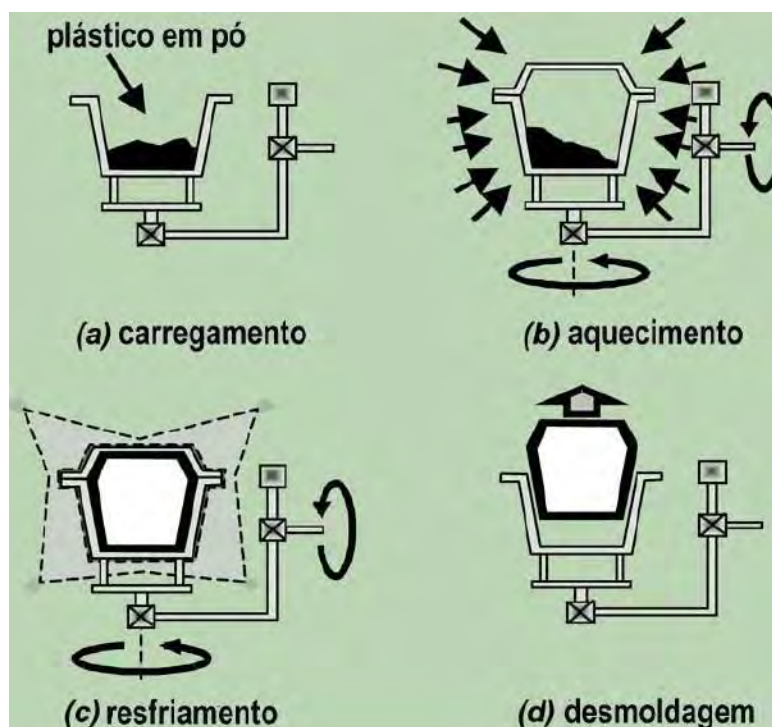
Processo de rotomoldagem.⁽⁵⁾
